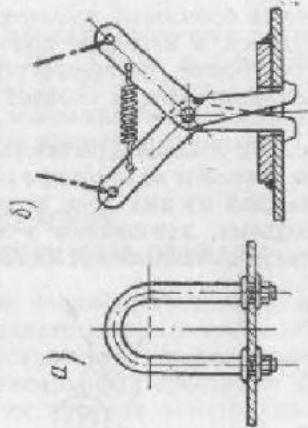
Приспособления для подъема секций через отверстия: а — скоба; б — рычажное приспособление.
